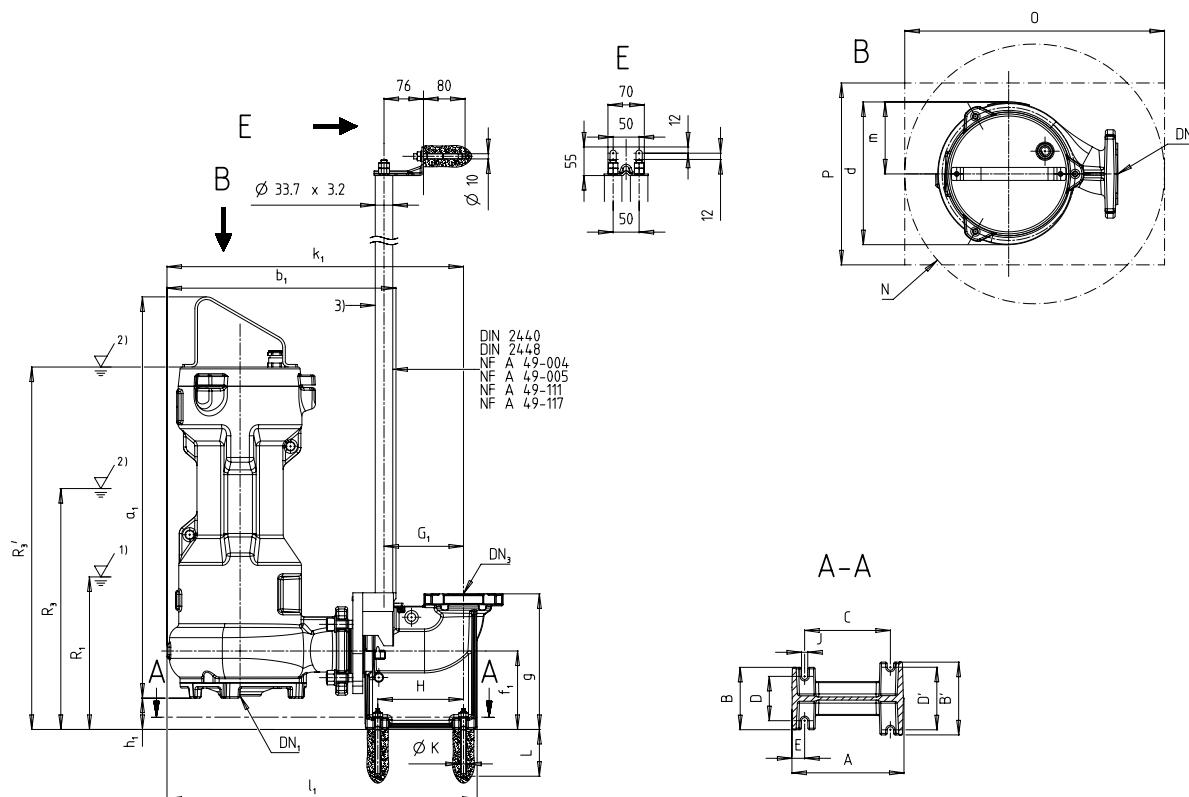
Amarex 65, instalação fixa, guiamento de 2 barras
